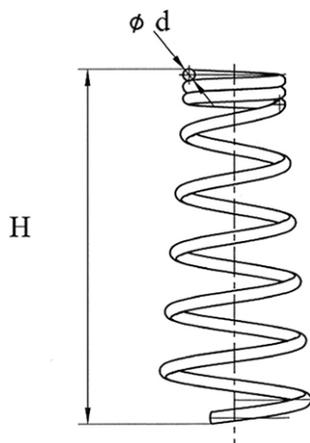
Спираль для армирования дюбеля железобетонного подрельсового основания [6]
